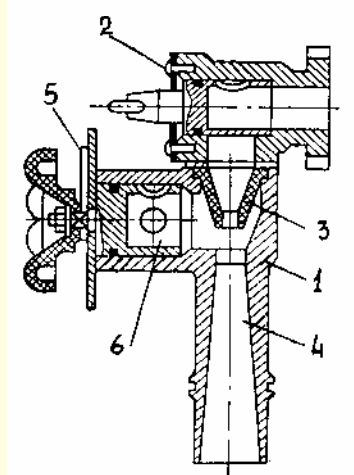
Пеносмеситель пожарного насоса ПС-5: 1 – корпус пеносмесителя; 2 – пробковый кран; 3 – сопло; 4 – диффузор; 5 – дозатор; 6 – калиброванная втулка
